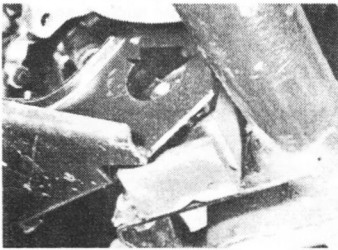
а. Расположение гайки правого крепления двигателя (указана стрелкой)...
